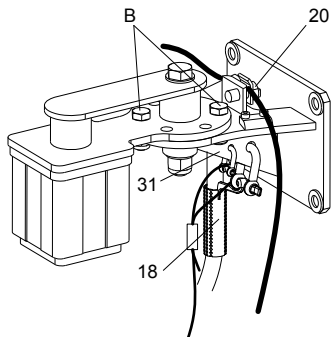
Верхний фиксатор с подъемным и страховочным тросами и кабельным разъемом
